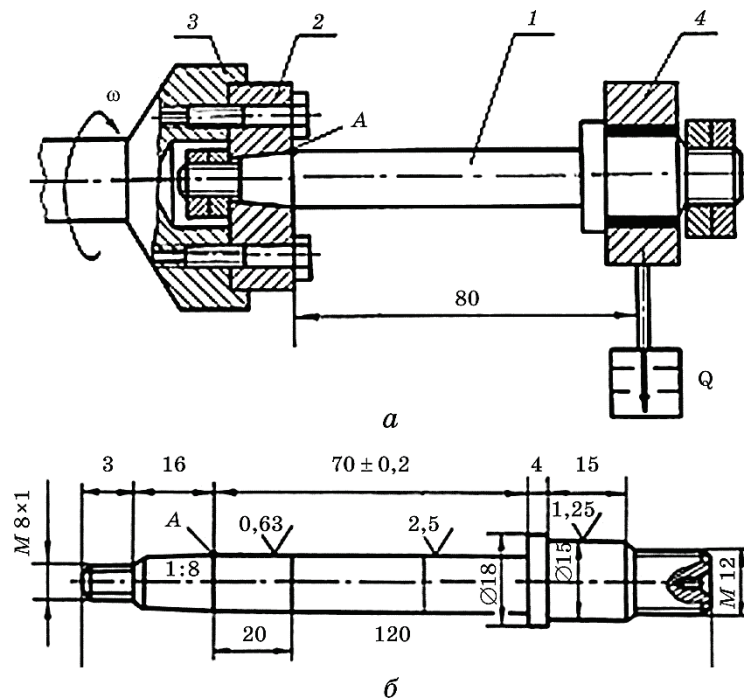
Схемы установки и образца для испытаний на фреттинг-усталость: 1 — испытываемый образец, 2 — контрообразец, 3 — держатель, 4 — нагрузочное устройство.
